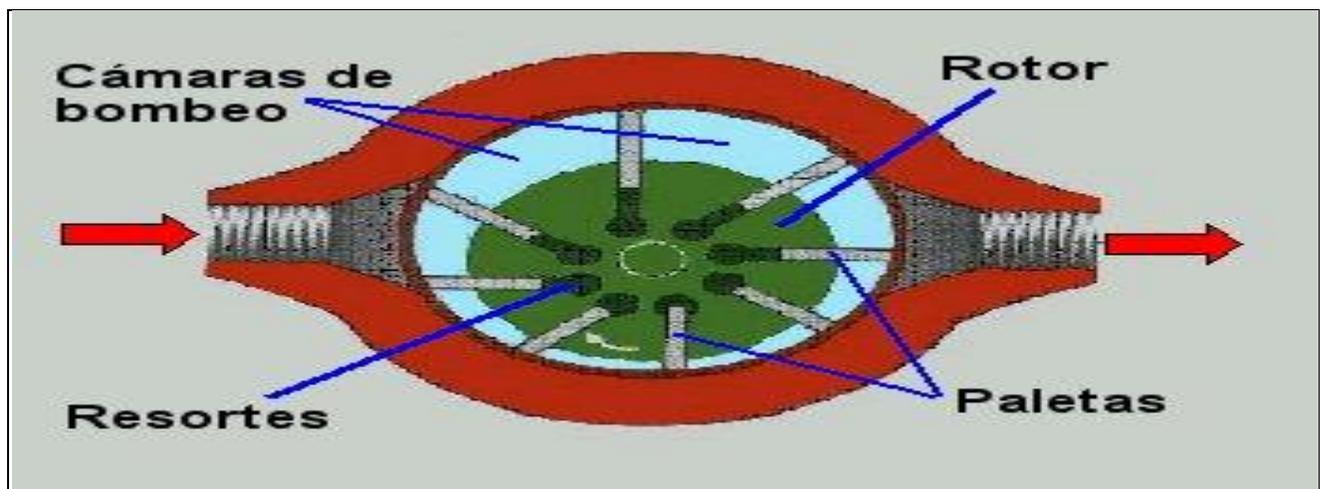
Bomba de Alabes o Paletas Parte a Lubricar
